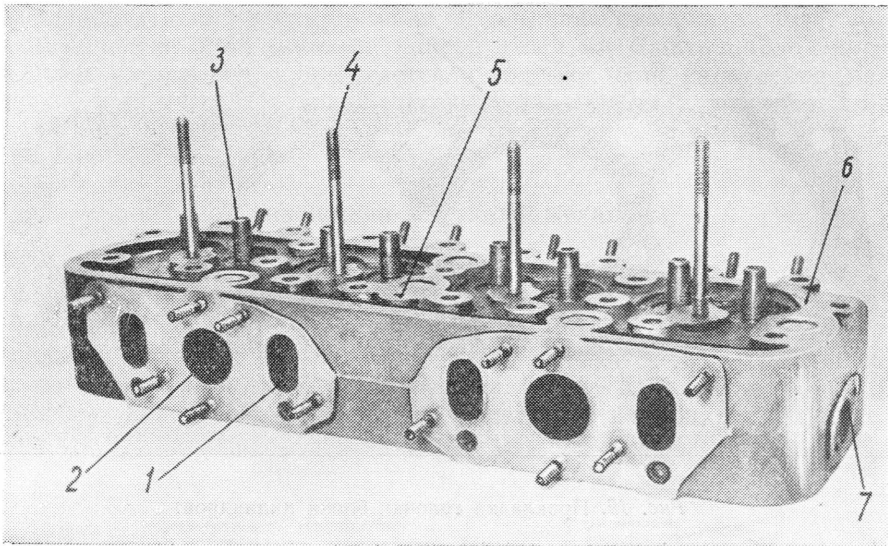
Головка блока цилиндров (вид сверху и сбоку):
